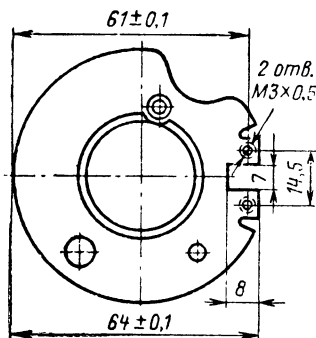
Чертеж доработанного подвижного диска прерывателя Р119.
